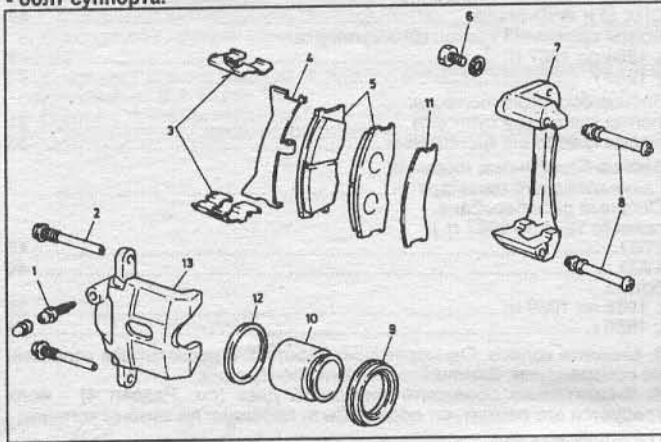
б Сборка переднего тормоза фирмы Sumitomo: 1 - штуцер прокачки; 2 - болт суппорта; 3 - фиксатор колодок; 4 - пластина фиксаторов; 5 - колодки; 6 - болт направляющей; 7 - направляющая колодок; 8 - втулка направляющей; 9 - пыльник; 10 - поршень; 11 - толкатель колодки; 12 - уплотнение поршня; 13 - суппорт.
